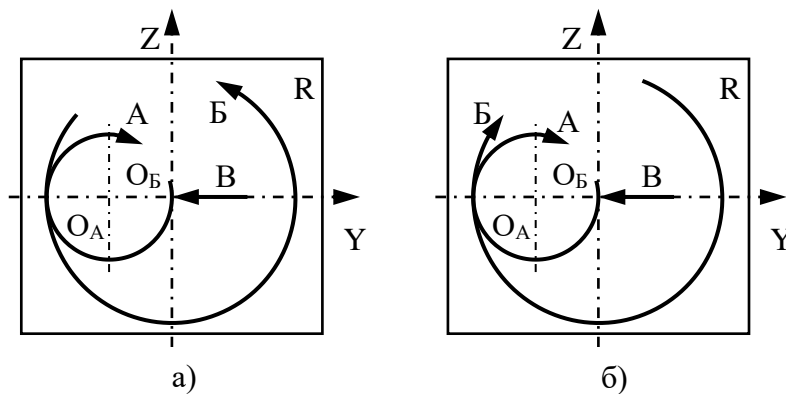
Елементарні рухи при внутрішньому відрізання обертових деталей фрезами для фрезерування:
